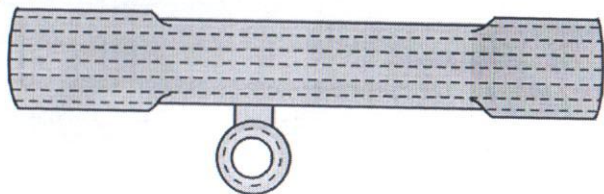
Контроль кронштейна и боковых поверхностей подвески тормозного башмака
